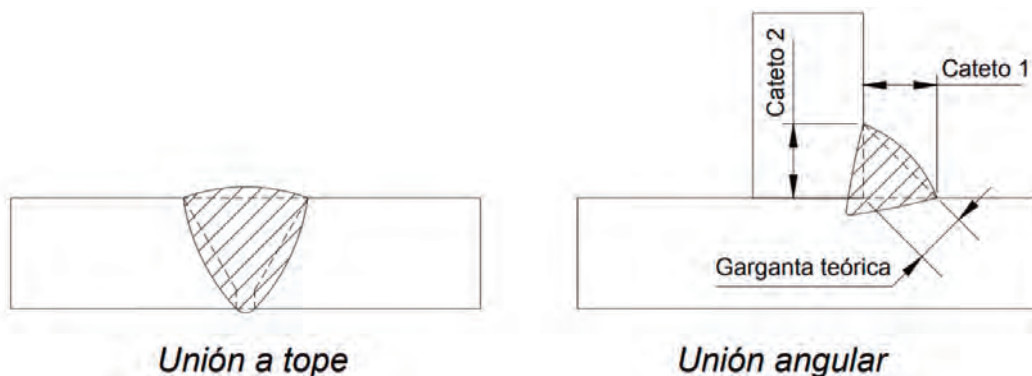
Tipos de uniones soldadas. Fuente: [11]
